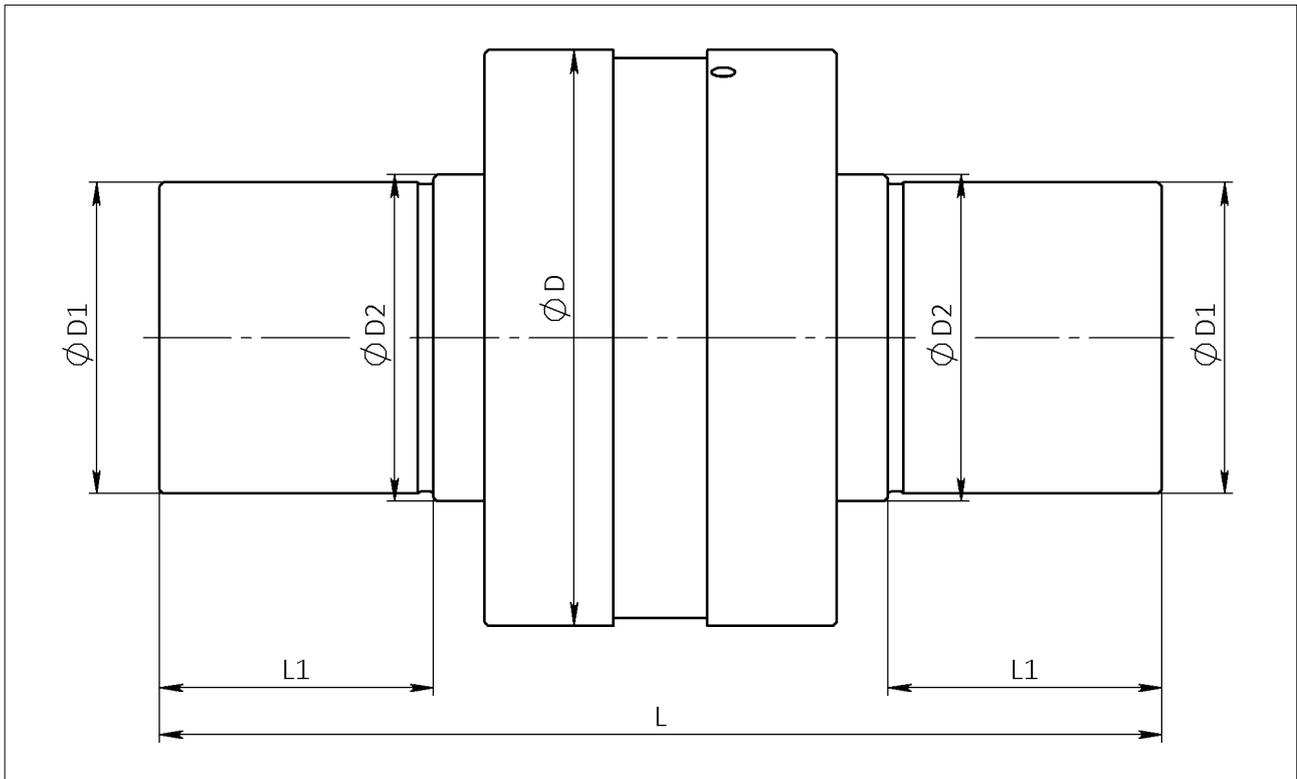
Ротор М26. Габаритные и установочные размеры, мм
